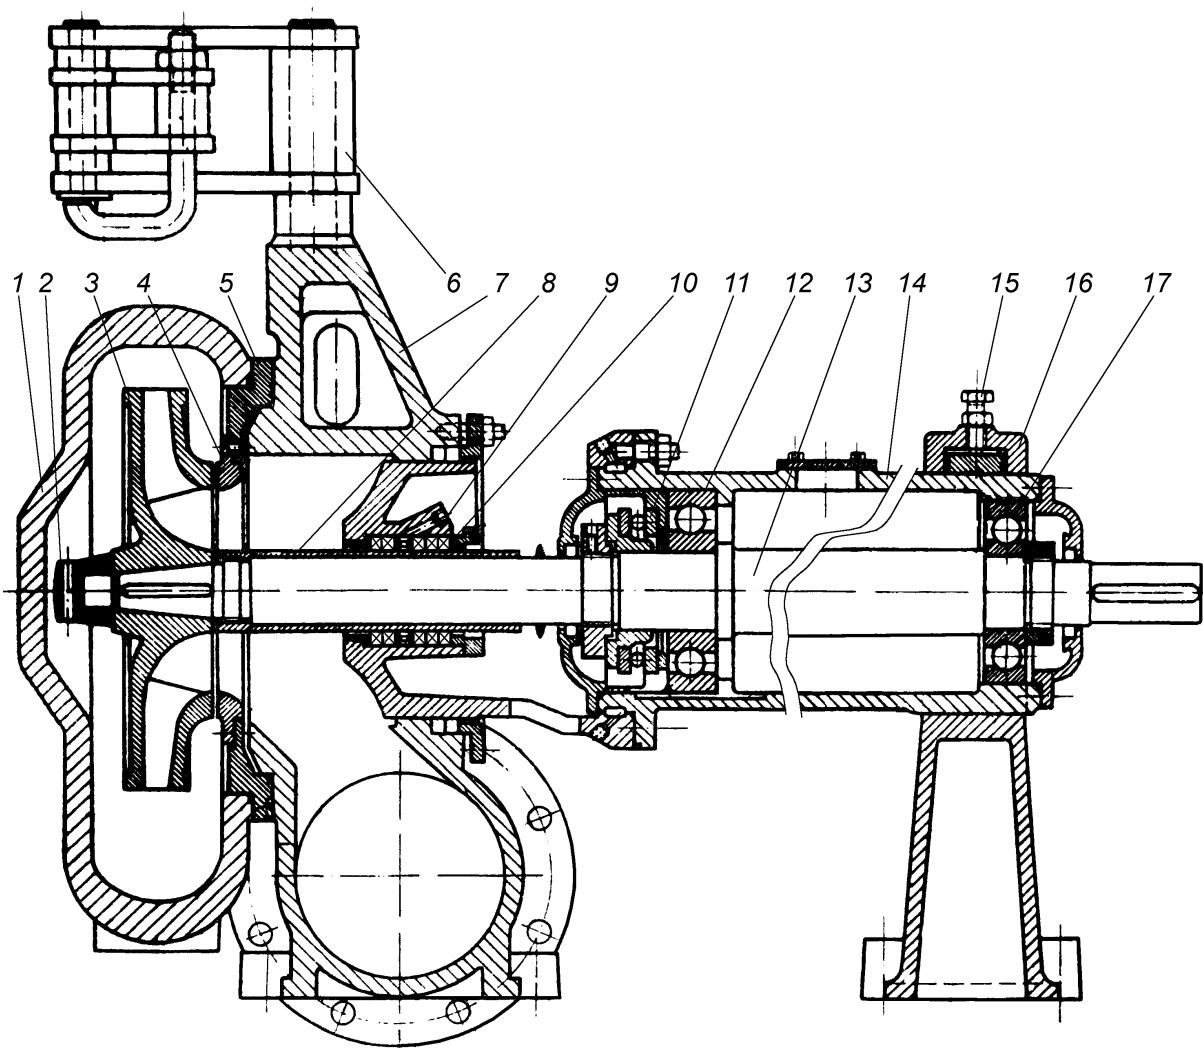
Цементний насос типу *NC* фірми *Sigma* (Чехія): 1 – спіральний корпус; 2 – гайка; 3 – робоче колесо; 4 – ущільнювальне кільце; 5 – вставка; 6 – підвісний пристрій; 7 – усмоктувальний корпус; 8 – захисна втулка; 9 – гідравлічний затвор; 10 – сальник; 11 – упорний шарикопідшипник; 12, 17 – радіальні шарикопідшипники; 13 – вал; 14 – кронштейн; 15 – настановний болт; 16 – стійка
